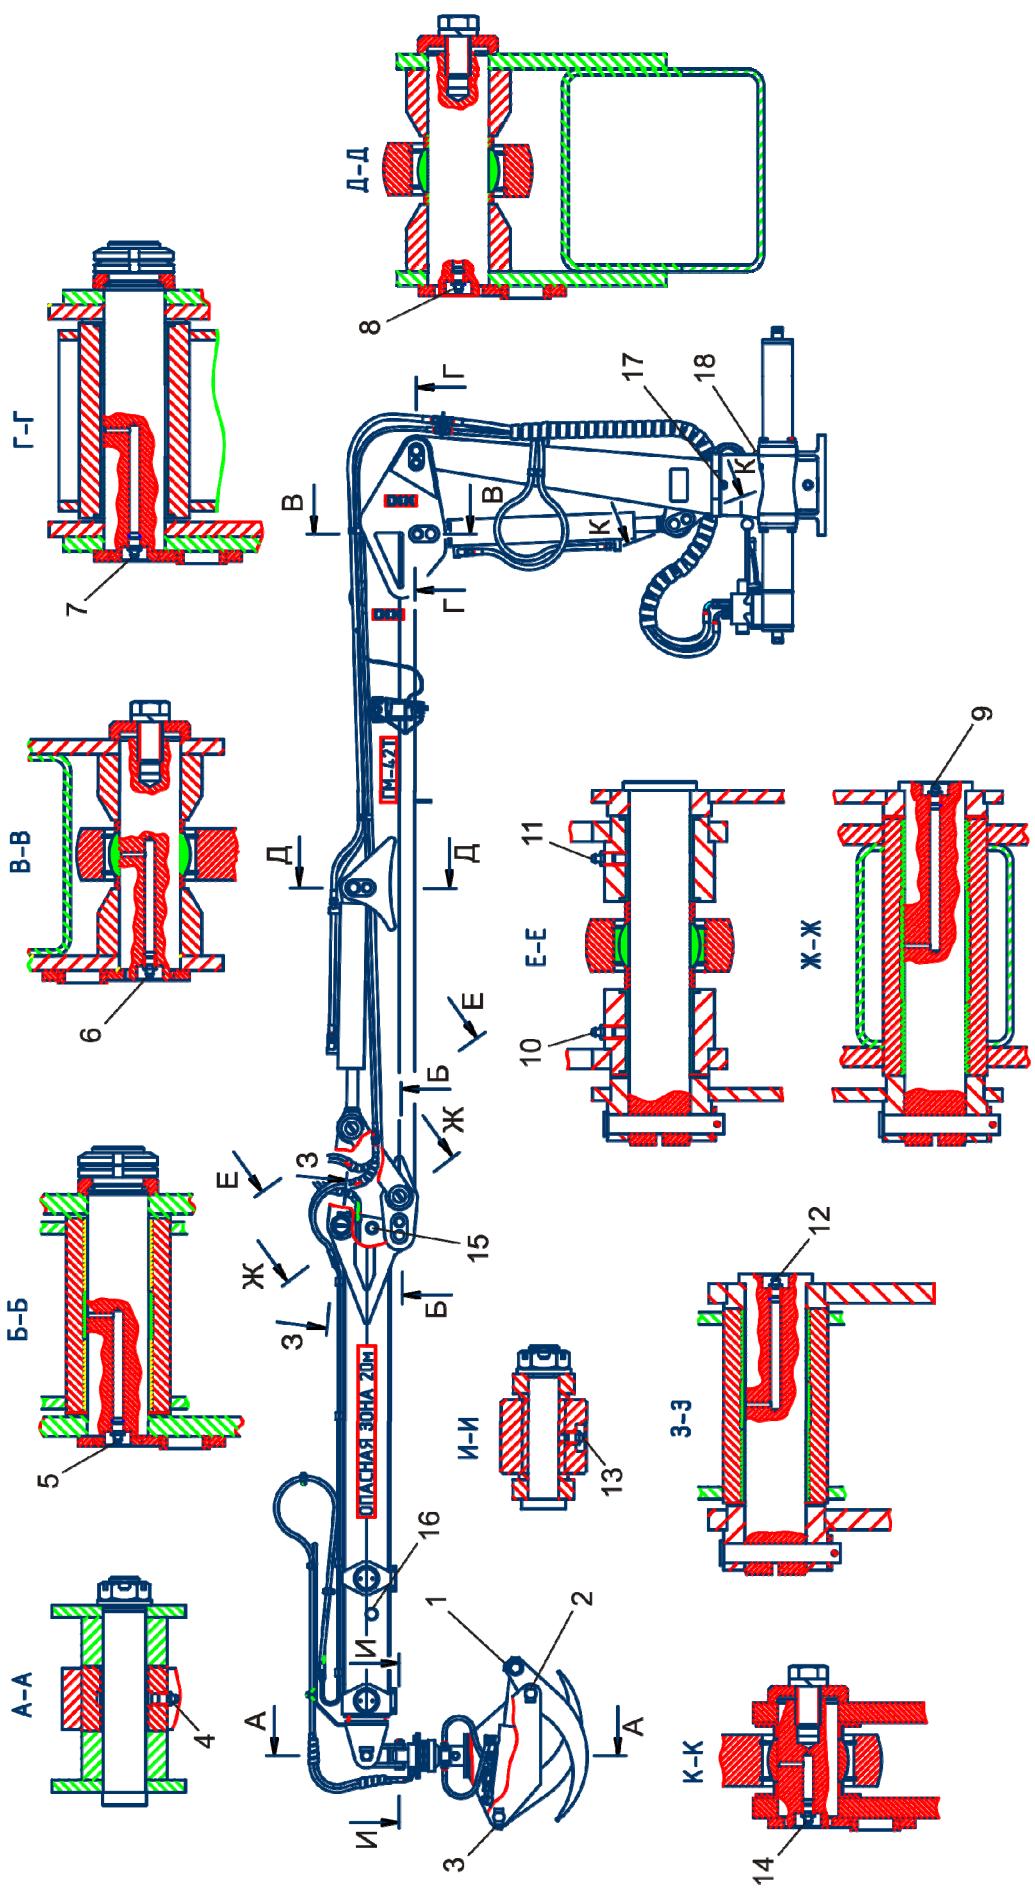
Схема смазки (заправки) манипулятора ГМ-50-01
